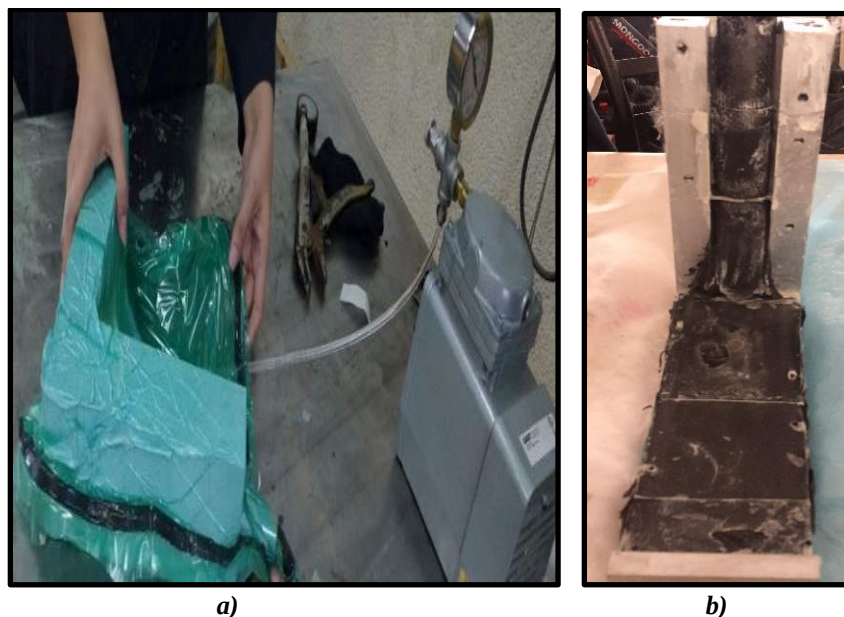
a) Pieza superior sometida a vacío; b) Pieza superior removida del molde.
